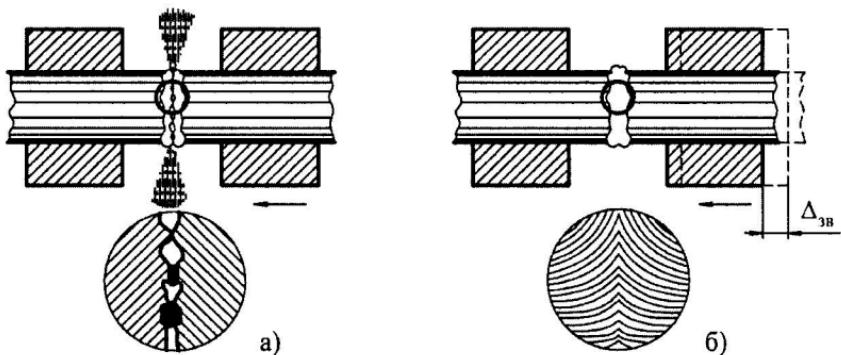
Схема процесу стикового зварювання оплавленням
